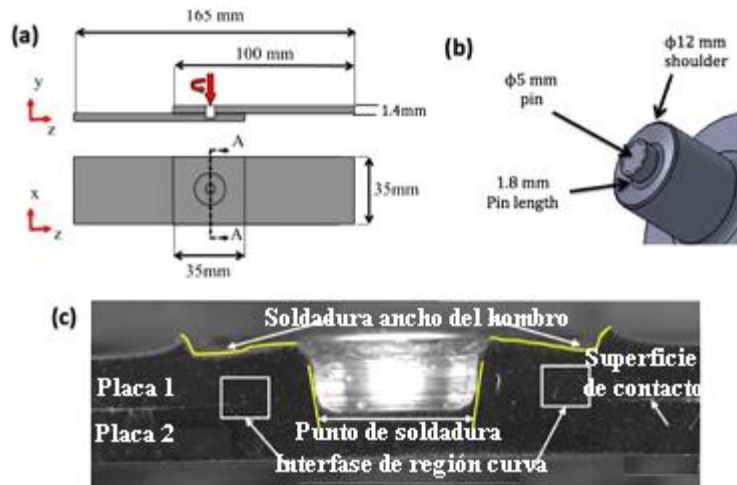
Esquema del proceso FSSW, a) configuración de la junta y dimensiones de las láminas, b) geometría de la herramienta utilizada y c) sección transversal del punto de soldadura mediante proceso FSSW.
